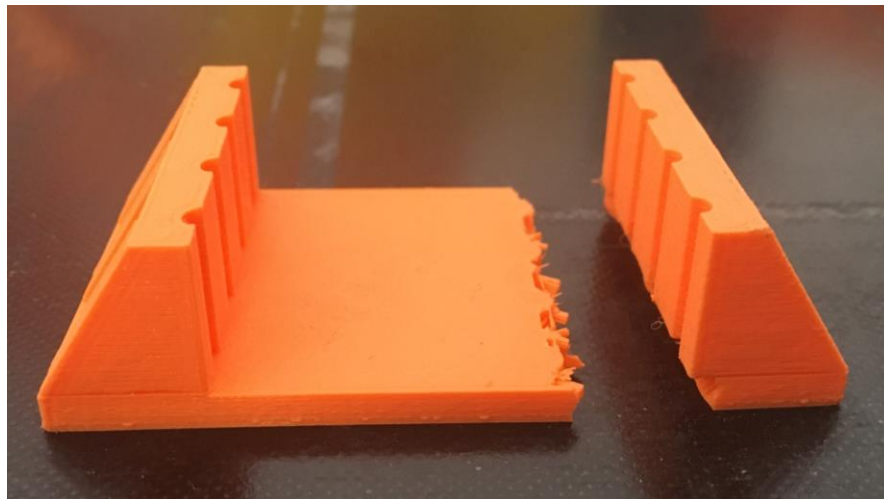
En la figura pueden verse las grietas entre las paredes verticales y el plano horizontal. Sin embargo, la rotura se ha producido por la base de la pieza, no por la grieta.
